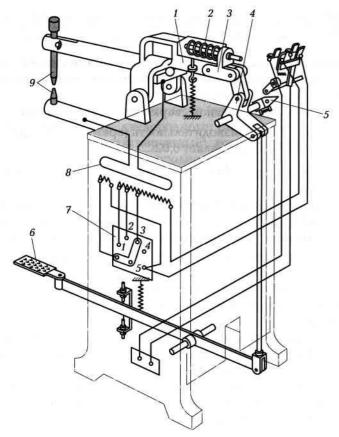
Контактная машина для точечной сварки:
